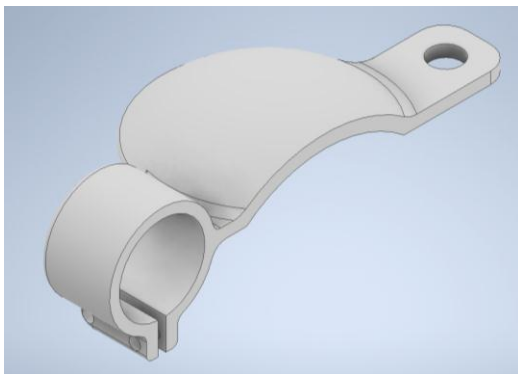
3D-модель деталі “Кріплення лазера”
